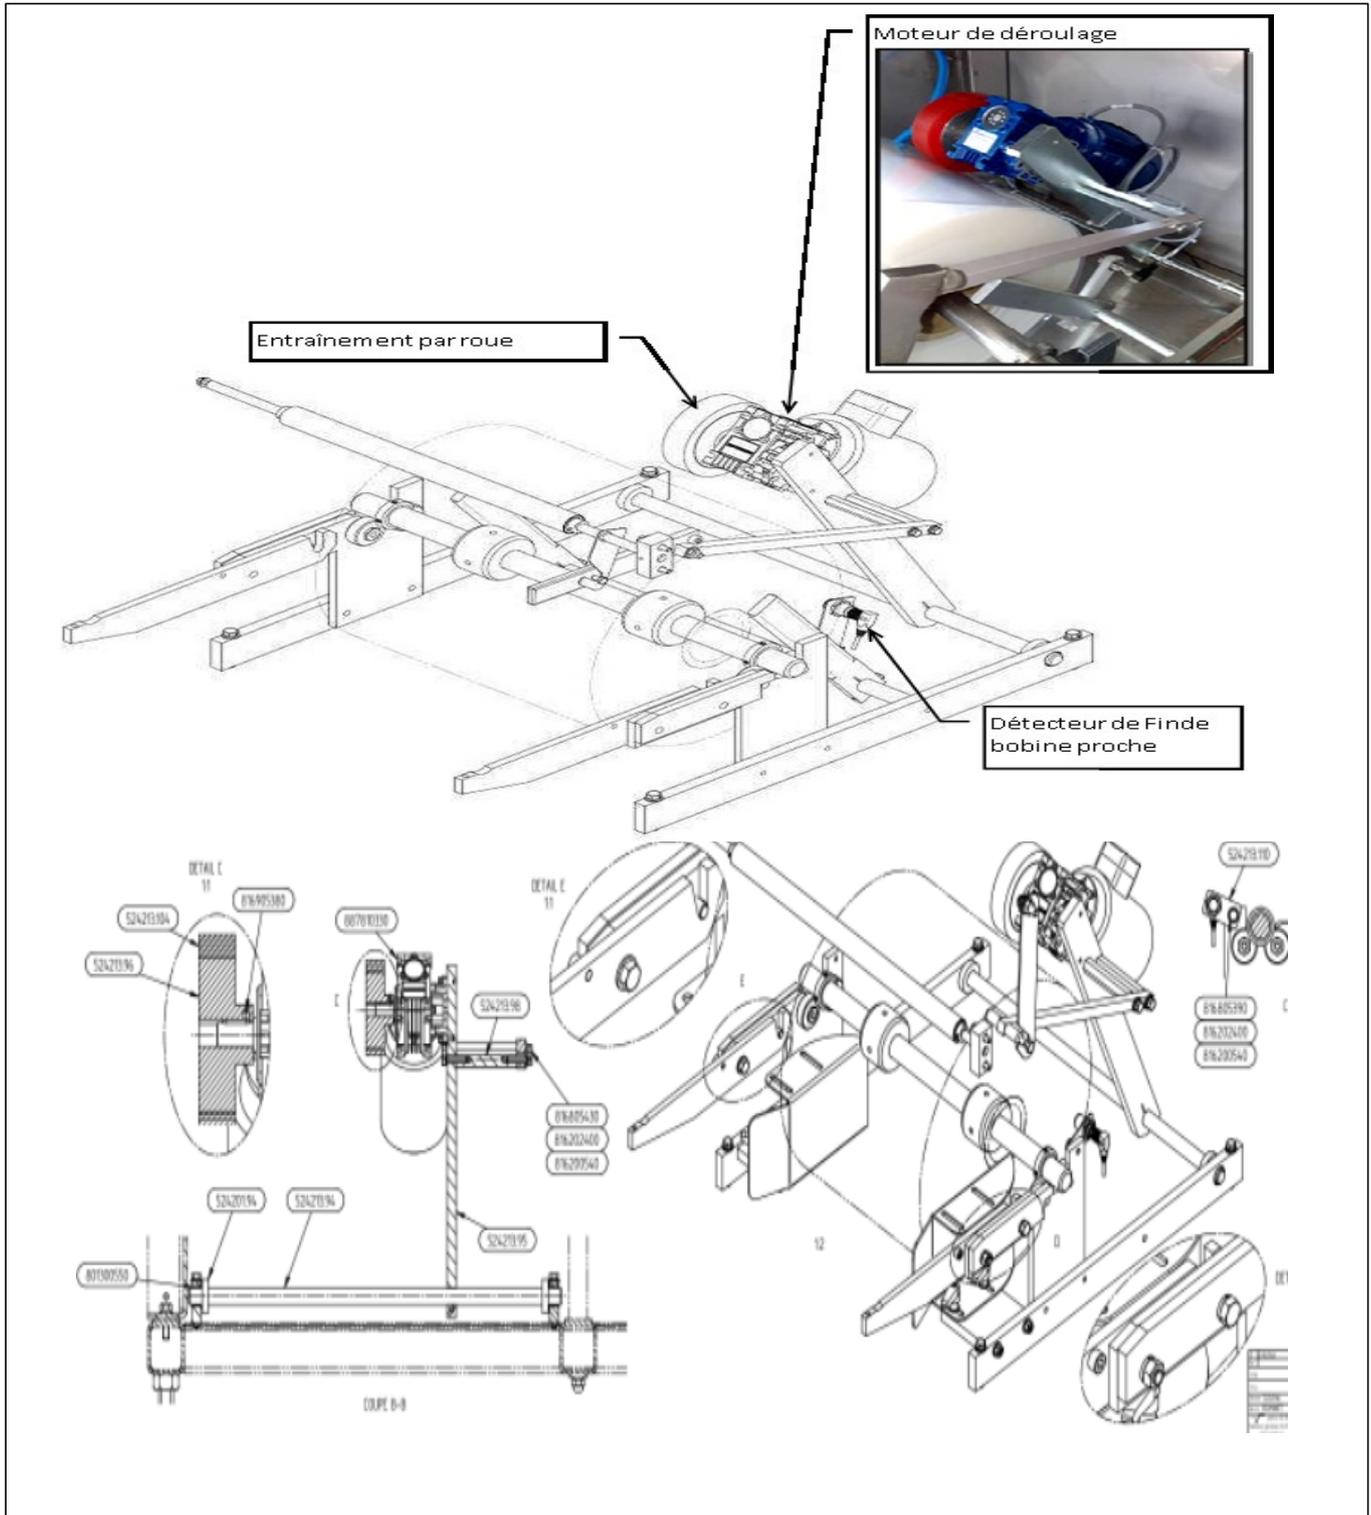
Figure III. 19:dessin technique pour le dérouleur de bobine.[16]
